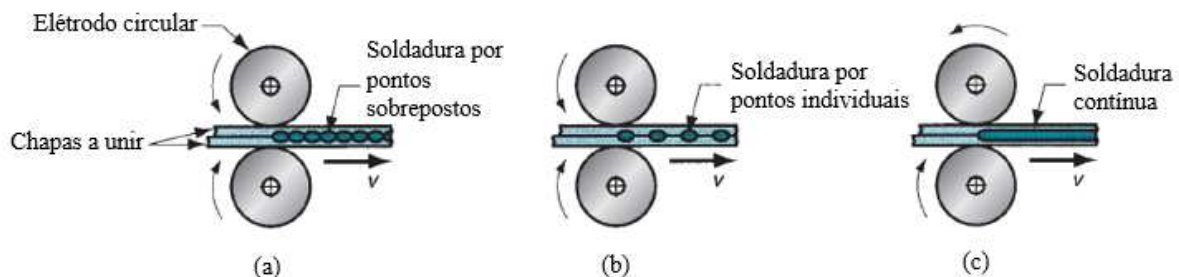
Diferentes tipos de soldaduras por roletes: (a) Soldadura por pontos sobrepostos; (b) Soldadura por pontos individuais; (c) Soldadura contínua (adaptação do original (Groover M., 2010)).
